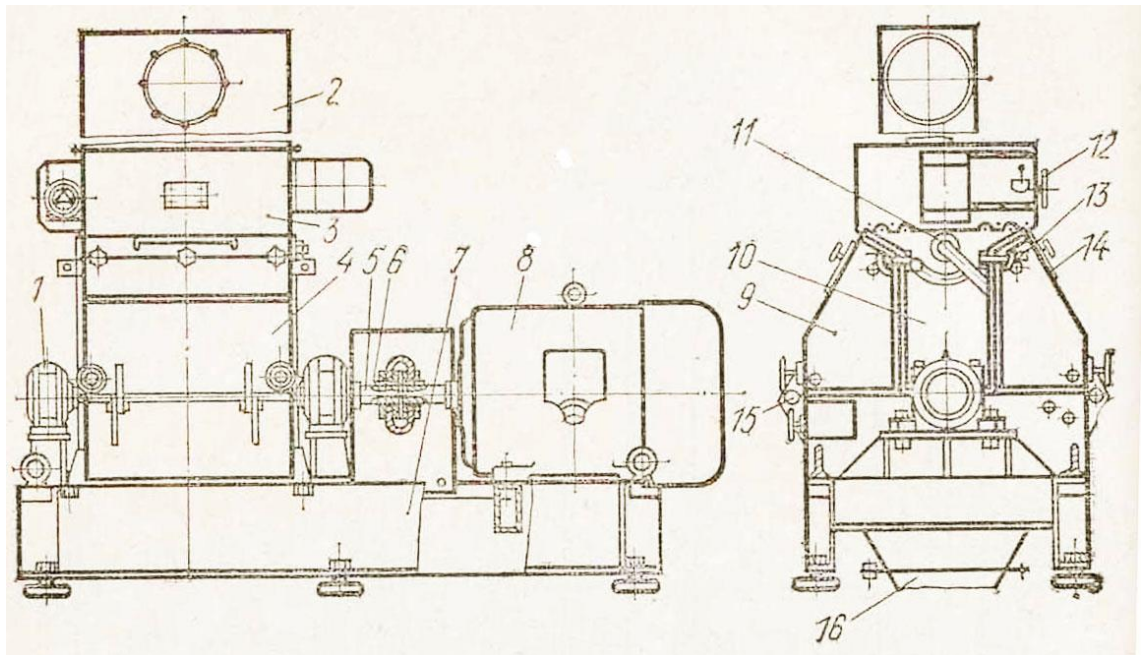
Молоткова дробарка А1-ДДР: 1 – підшипник; 2 – розширююча камера; 3 – живник; 4 – основа; 5 – вал; 6 – муфта; 7 – станина; 8 – електродвигун; 9 – кришка; 10 – середня частина корпусу; 11 – важиль; 12 – механізм регулювання; 13 – бовт; 14 – дверцята; 15 – петля; 16 – бункер» [9].
